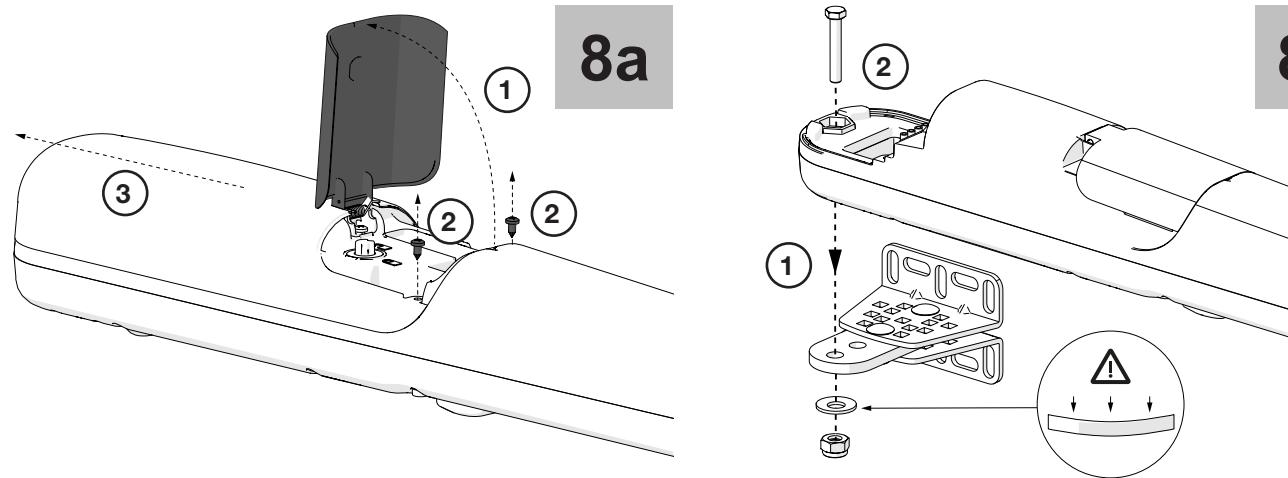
FR - Fixation du motoréducteur et du chevron avant
